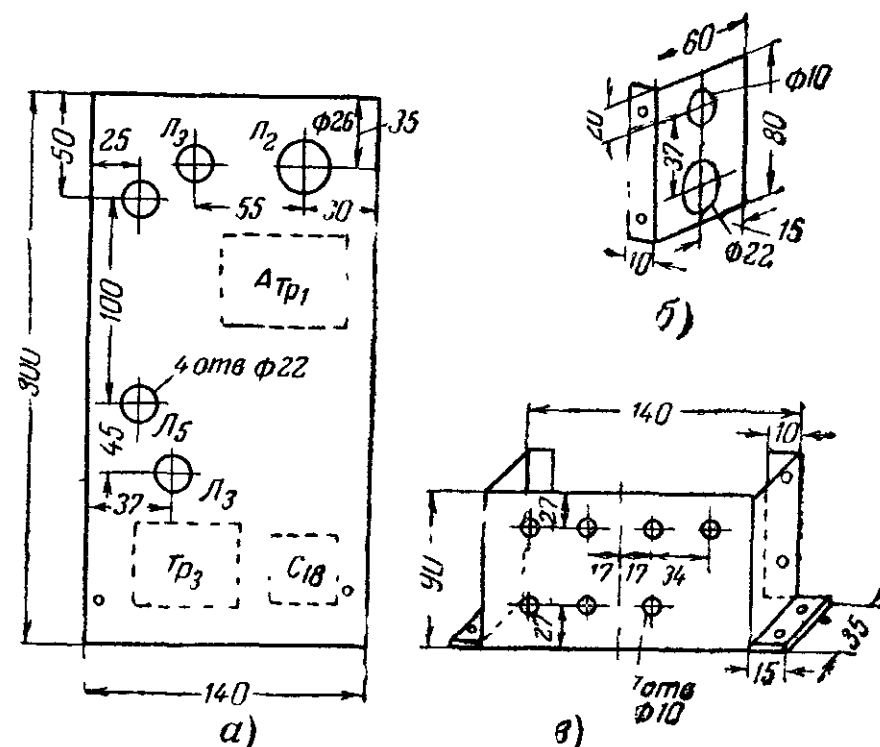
Детали шасси блока развертки с нормализованными деталями.
